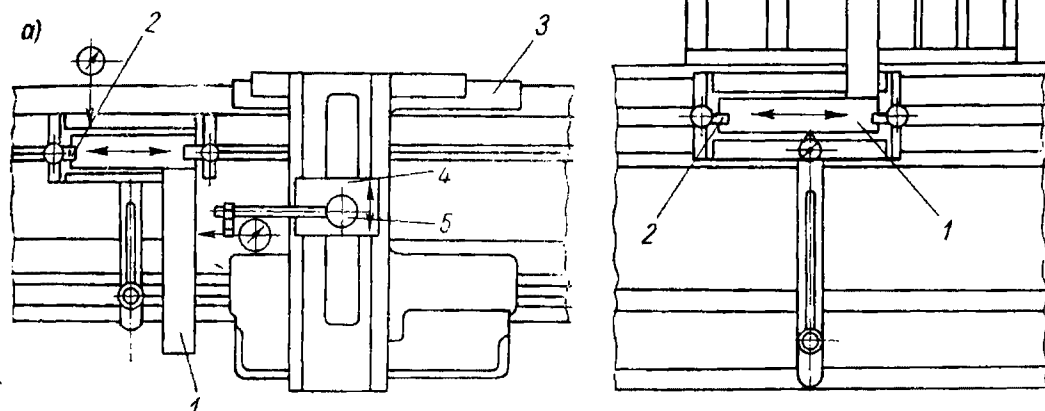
Схема проверки перпендикулярности направляющих: а — каретки суппорта токарного станка; б — станины круглошлифовального станка
